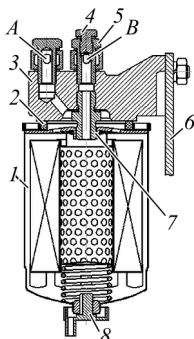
Фильтр тонкой очистки топлива: 1 – фильтр неразборный; 2 – прокладка; 3 – корпус; 4 – пробка для выпуска воздуха; 5 – штуцер отводящий; 6 – кронштейн; 7 – штуцер; 8 – пробка для слива отстоя; А – подвод топлива; В – отвод топлива
